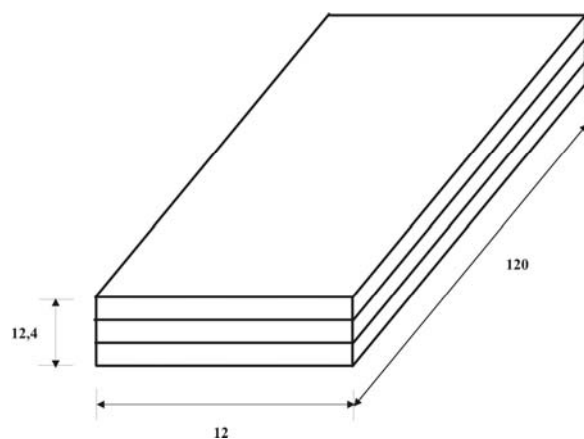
Dimensões, em mm, do corpo de prova na configuração de impacto na superfície da placa
